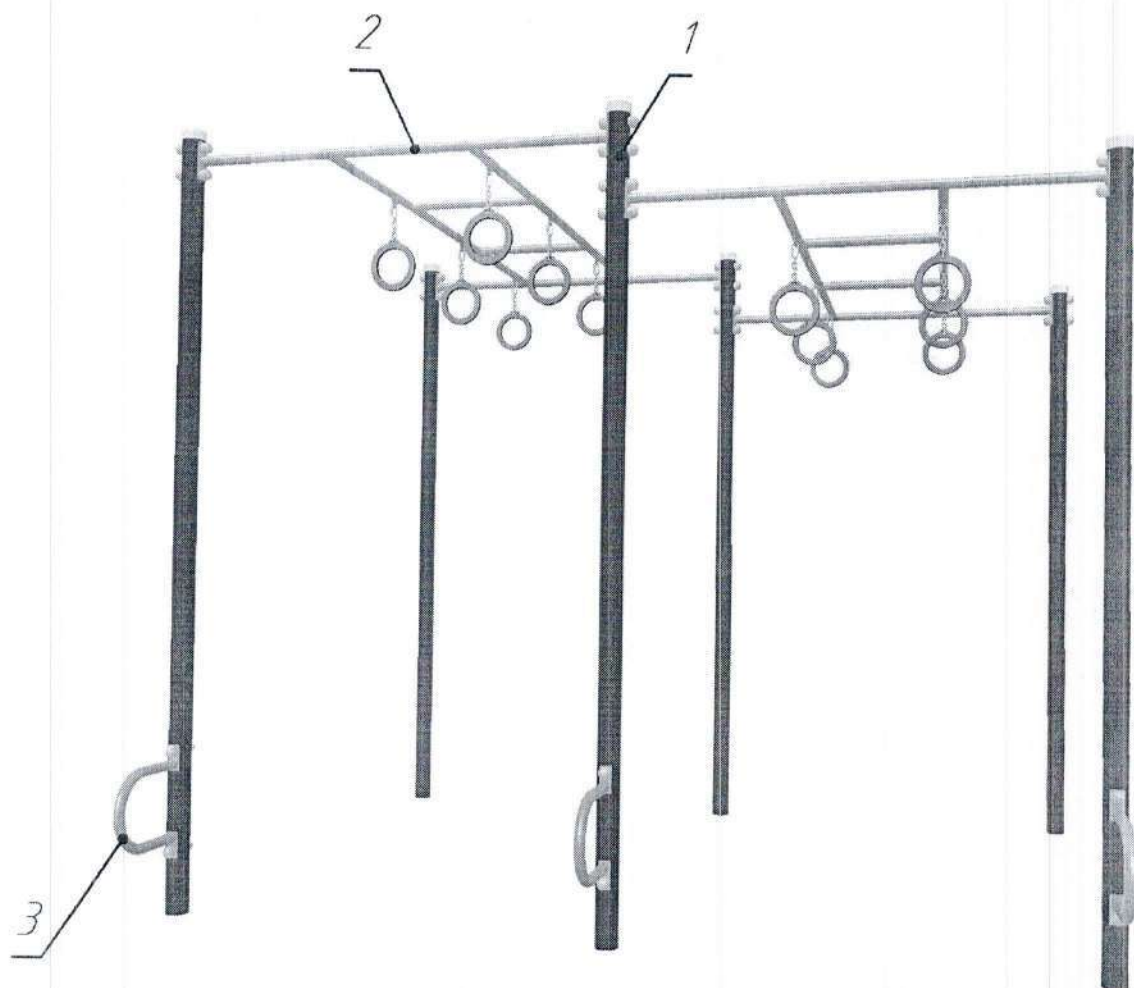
Общий вид Рукохода с кольцами двойного РТР 729D
